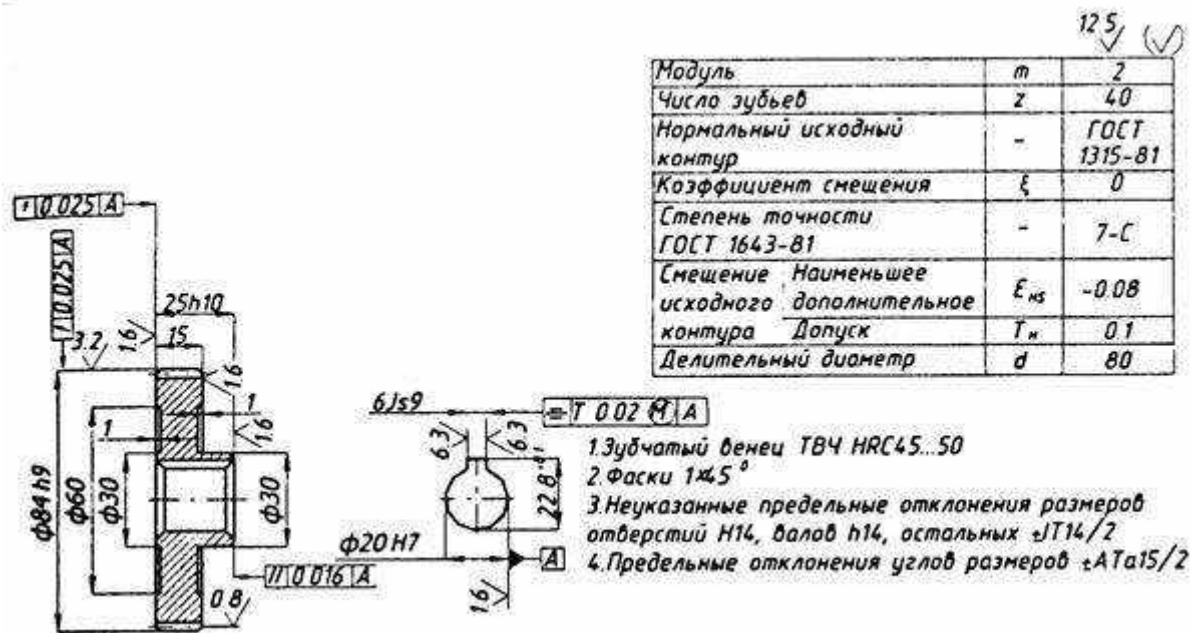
Типовое цилиндрическое зубчатое колесо с односторонней ступицей
